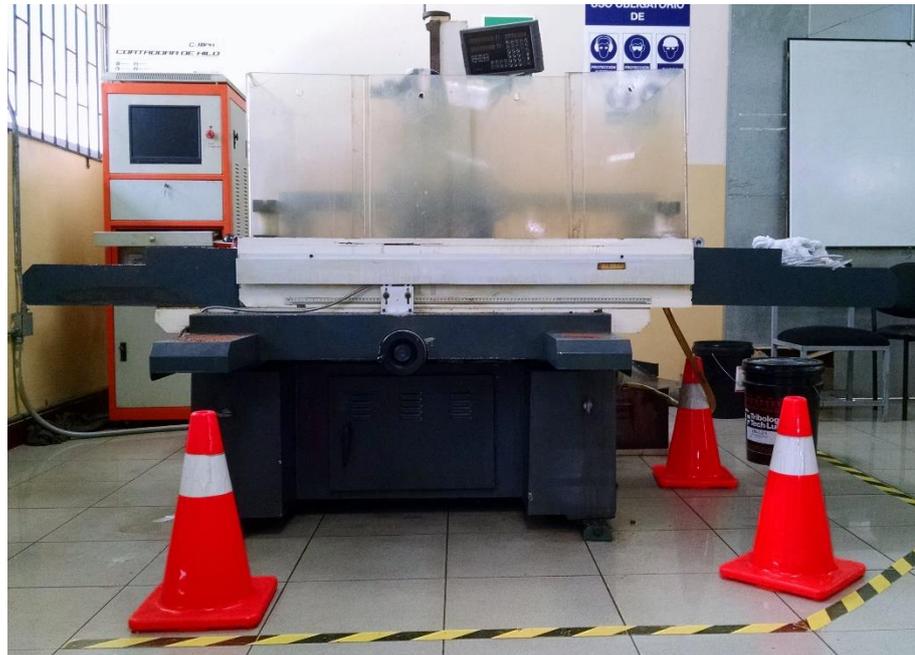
Cortadora de Hilo CNC del Laboratorio CAMPRO
